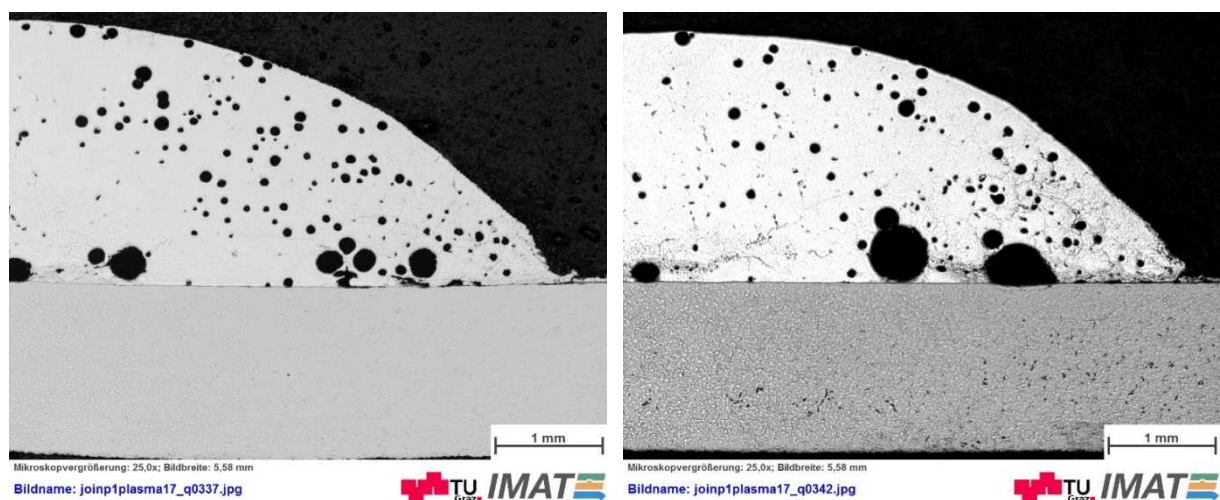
Querschliffe der Schweißnähte aus den Versuchen 31-Nahtende (links) und 34-Nahtanfang (rechts)
